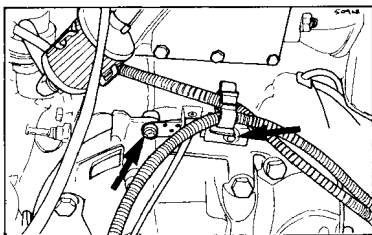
Болты крепления датчика углового положения коленчатого вала (отмечены стрелками)
